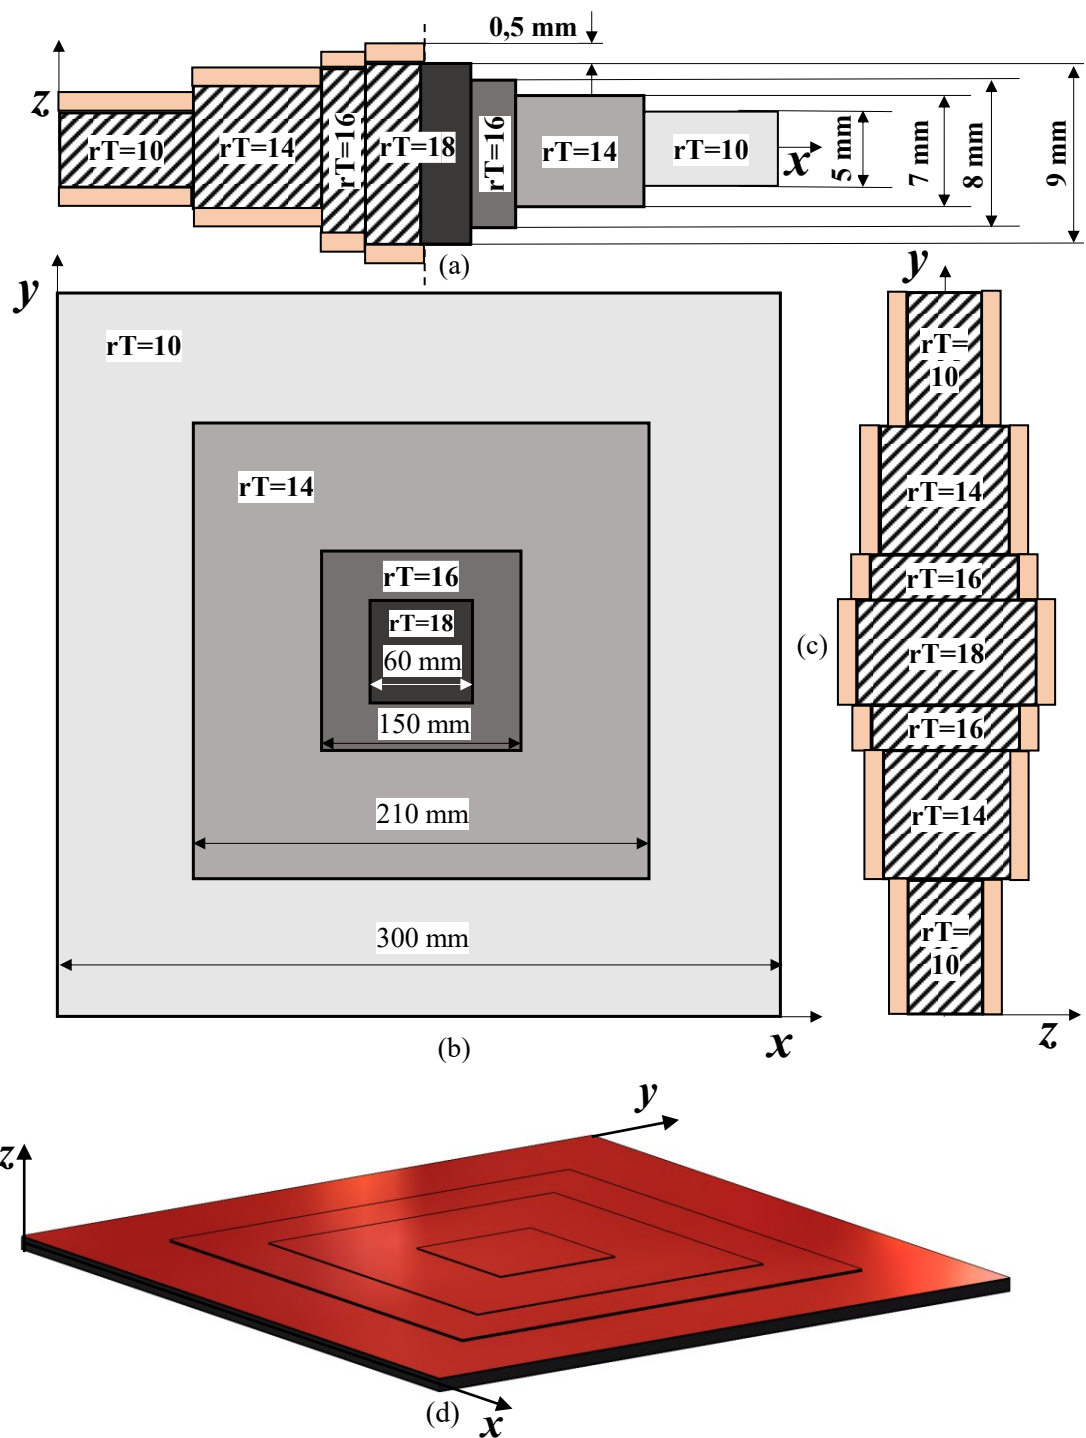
Representação esquemática isométrica do Tapering-2 (2D) da placa e nas vistas: (a) Vista Lateral (plano xOz); (b) Vista em Planta (plano xOy); (c) Vista Lateral (plano yOz); (d) Vista isométrica.
